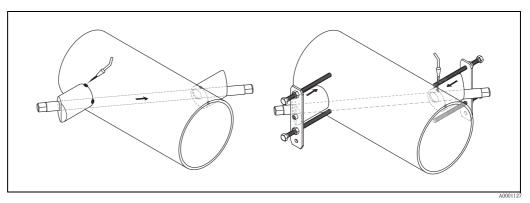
Montaggio dei sensori di misura, fasi 7 e 8
